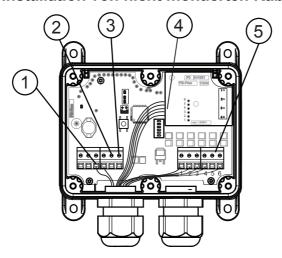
Sesam 800 RXM 12/24 V DC für Winde von Geländefahrzeug ohne Kabel
